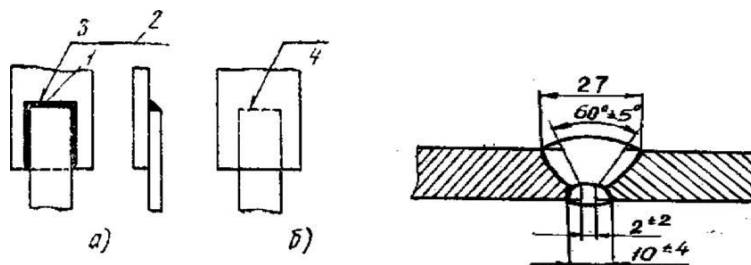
Условное изображение сварных швов:
